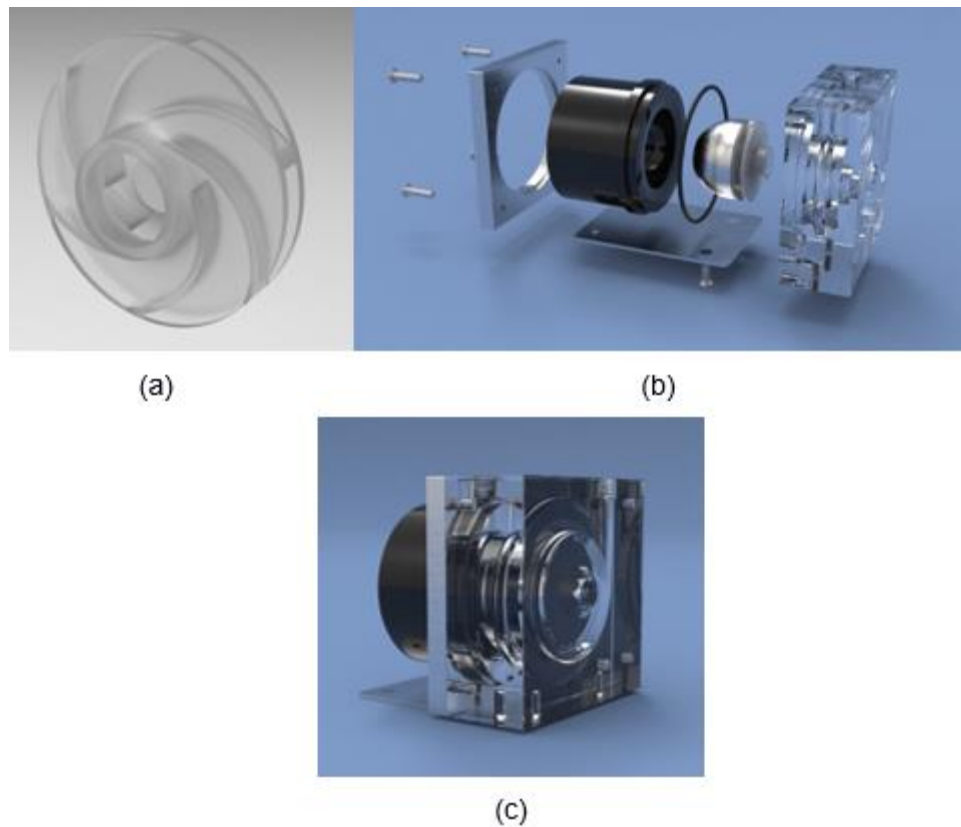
(a) vista del impulsor (b) vista explotada (c) vista del ensamble.
